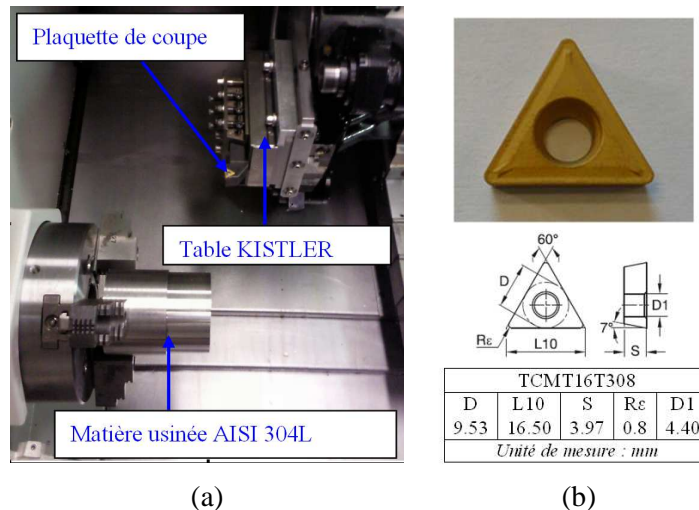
Dispositif expérimental (a), géométrie de la plaquette de coupe (b).
